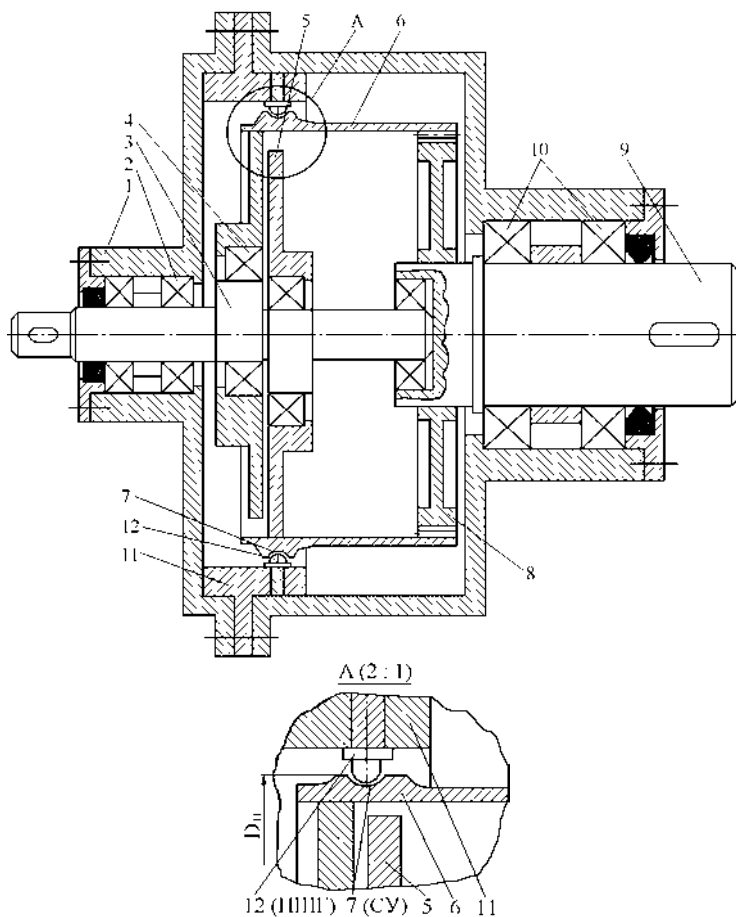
Конструктивная схема волновой шариковой передачи (ВШП): 1 – корпус; 2 – подшипники; 3 – эксцентриковый вал; 4 – подшипники; 5 – диски; 6 – гибкое колесо; 7 – сферические углубления; 8 – шлицевое соединение; 9 – выходной вал; 10 – подшипники; 11 – жесткое колесо; 12 – пальцы с шарообразными головками
